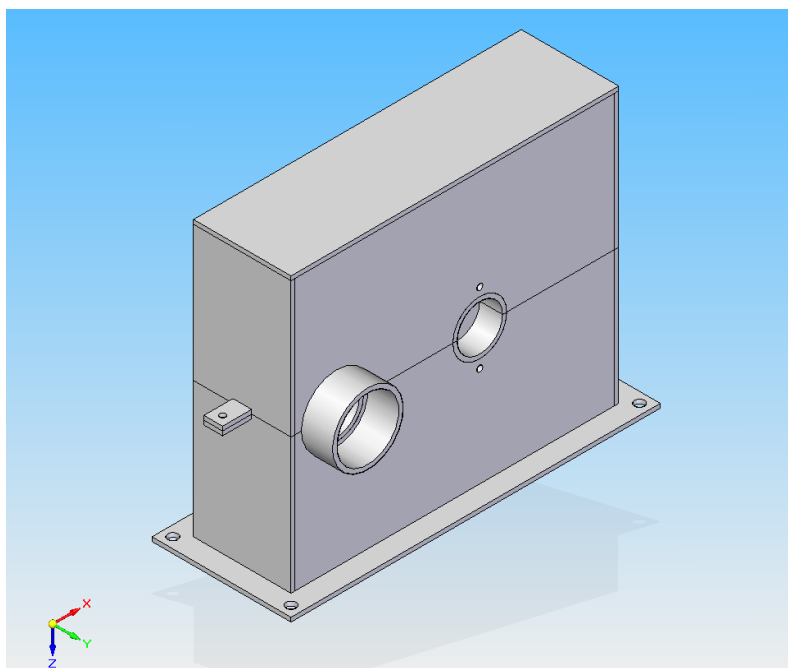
Caixa da redução construída com chapas soldadas para redução de custos
